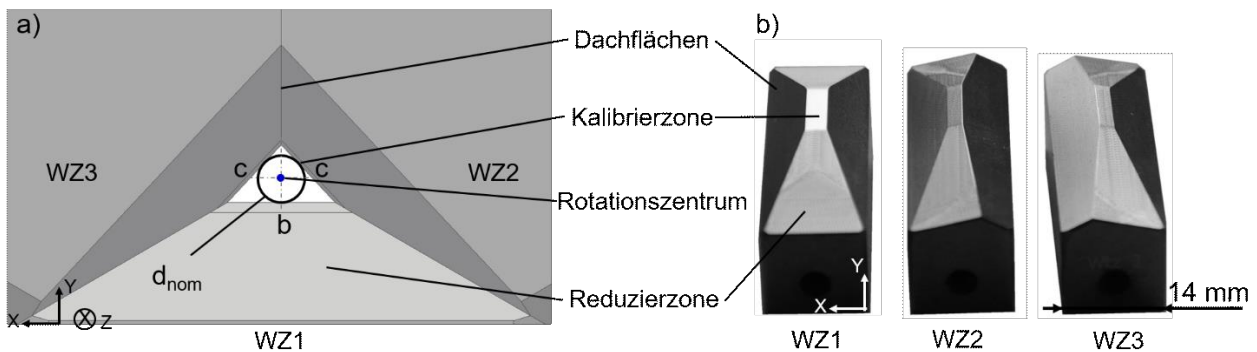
Werkzeugkonzept exzentrischer Werkzeuge: a) Bildung eines ungleichseitigen Dreiecks durch drei Flächen der EW in der Kalibrierzone; b) Werkzeugsatz bestehend aus drei Flachwerkzeugen.
